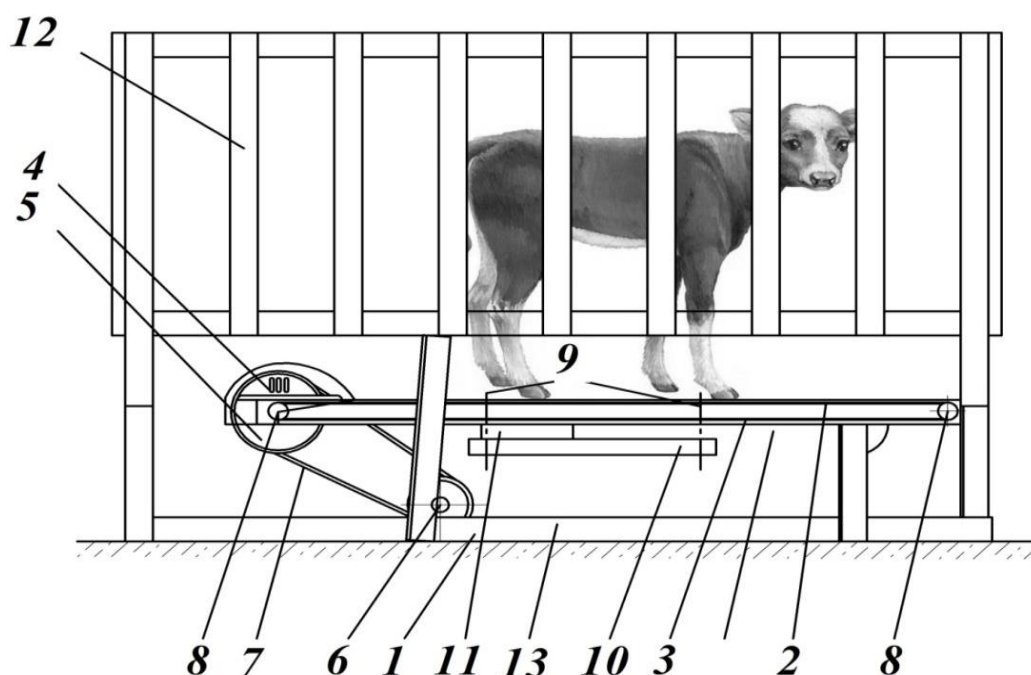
Клетка для содержания телят: 1 – рама клетки; 2 – рама подвижной ленты; 3 – подвижная лента; 4 – электродвигатель; 5 – ведущий шкив; 6 – ведомый шкив; 7 – ремень; 8 – натяжные ролики; 9 – шпильки; 10 – рамка; 11 – скребок очищающего устройства; 12 – деревянная клетка
